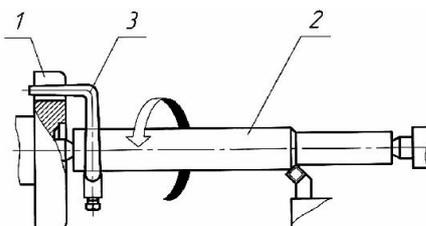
Заготовка инструмента, установленная в центрах: 1– планшайба; 2– заготовка инструмента; 3– хомутик
